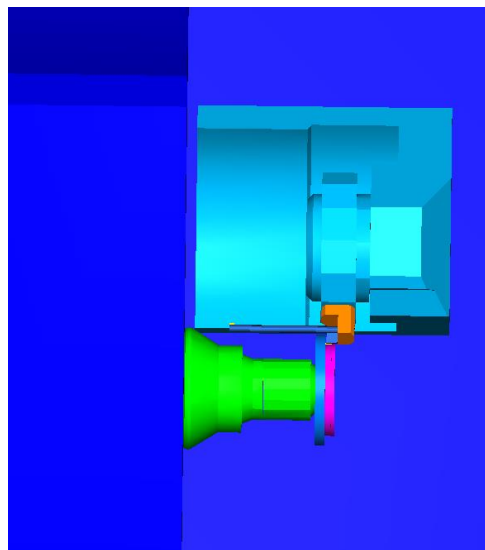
Процес обробки деталі «Зірочка»
